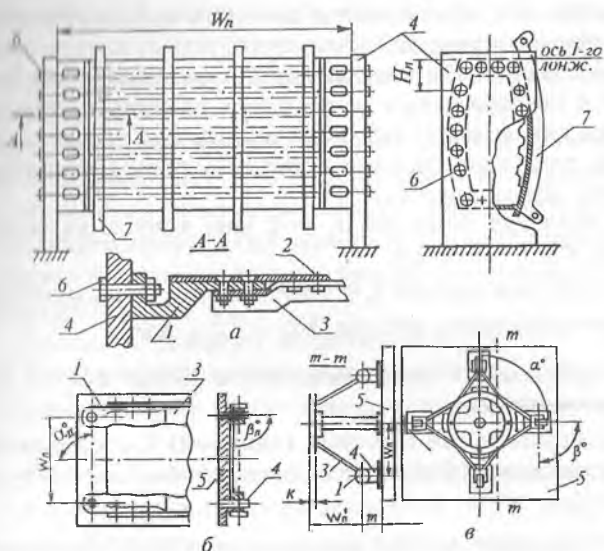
Схемы базирования по ОСБ: а — сборка по ОСБ кессона центроплана; б — сборка лонжерона; в — сборка моторами; г — стыковой узел; 2 — обшивка; 3 — элементы каркаса изделия; 4 — базовые поверхности приспособления; б — каркас приспособления; б — штырь (технологический болт); 7 — рубильник
